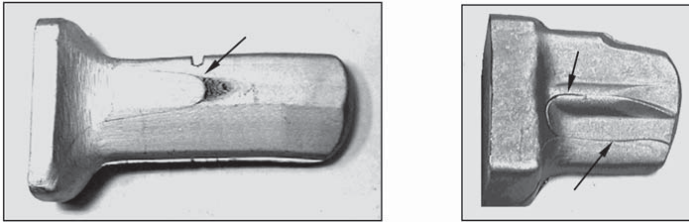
Виробничий дефект у вигляді розшарувань металу під час штампування проміжної заготовки лопатки газотурбінного двигуна
